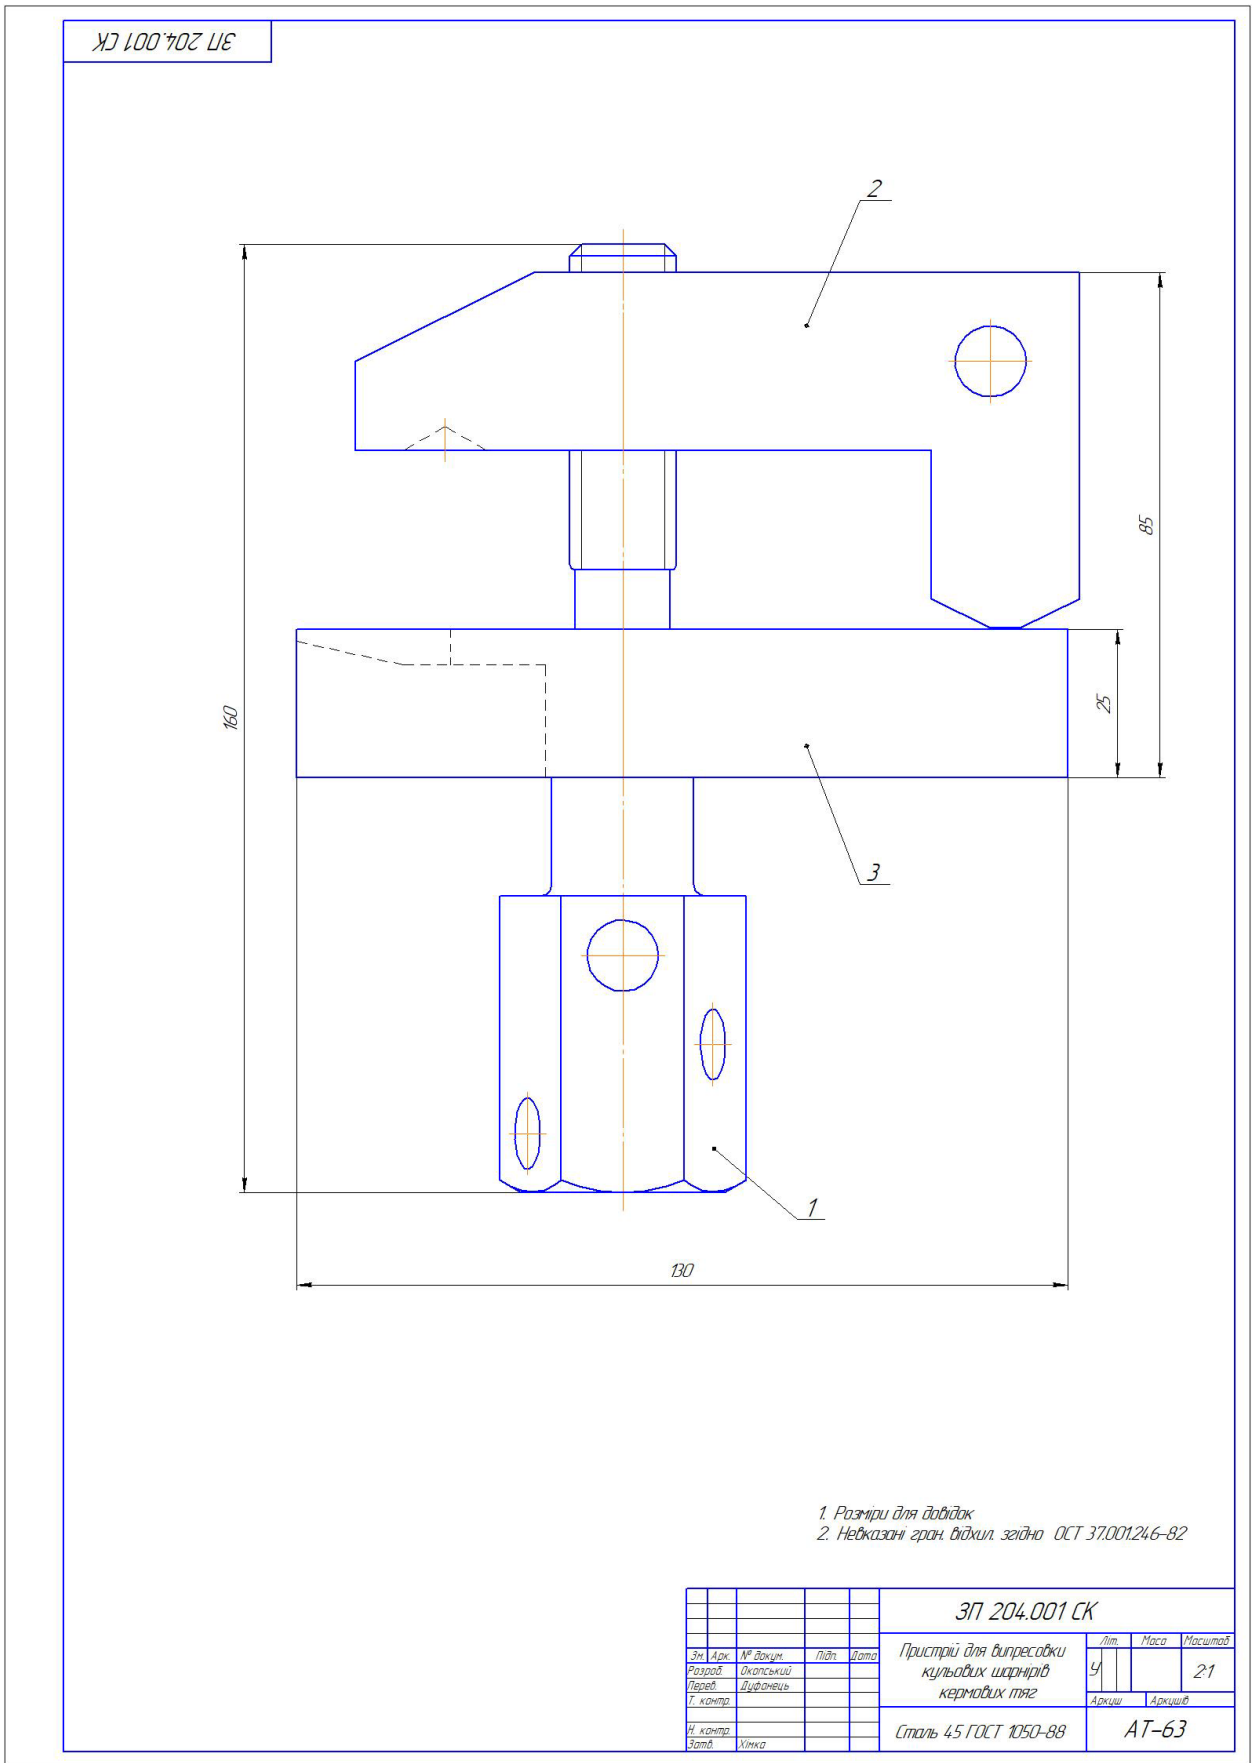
Пристрій для випресовки кульових шарнірів кермової тяги складальне креслення.
